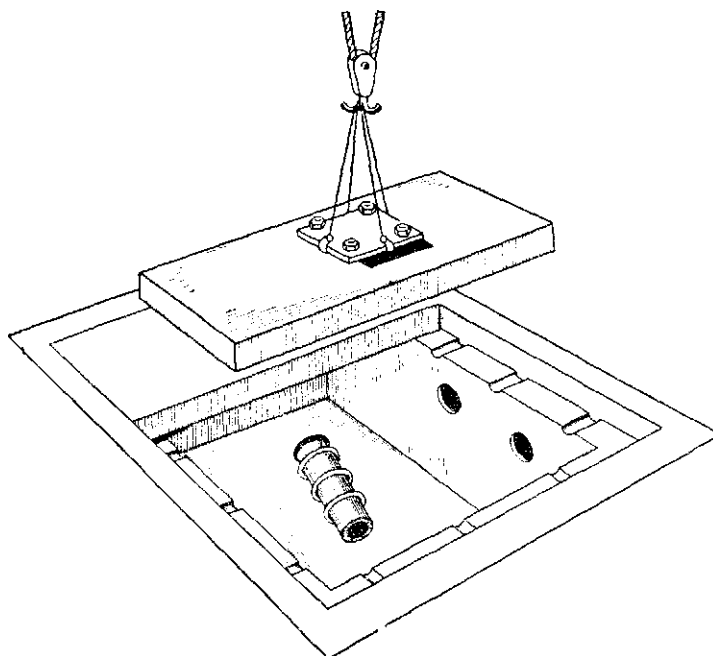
Железобетонная взрывная яма для промышленного взрывания стали и железа
